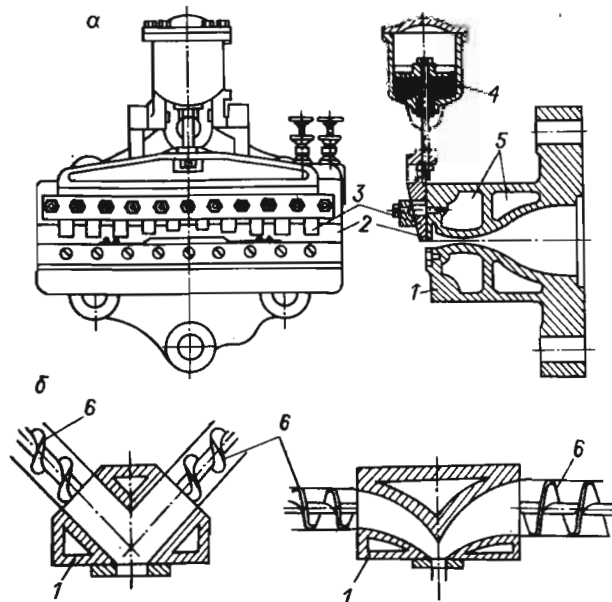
Схема головки червячного пресса для профилирования протекторных заготовок (а) и работа двух червячных прессов с общей головкой (б): 1 — корпус головки; 2 — профильная планка; 3 — конусная зажимная гребенка; 4 — пневмоцилиндр; 5 — полость для нагрева или охлаждения; 6 — червяк
